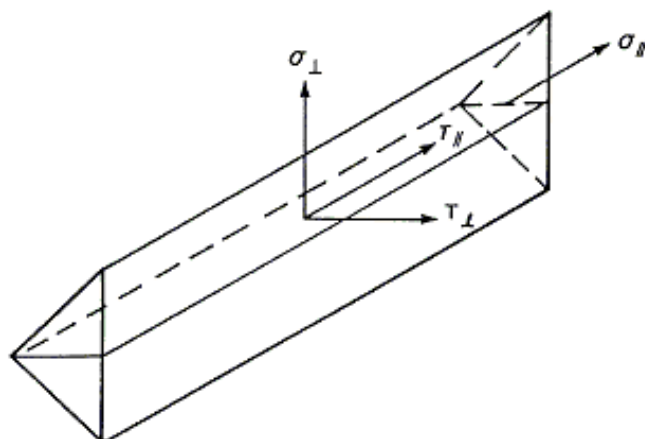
Напряжения в поперечном сечении углового сварного шва
